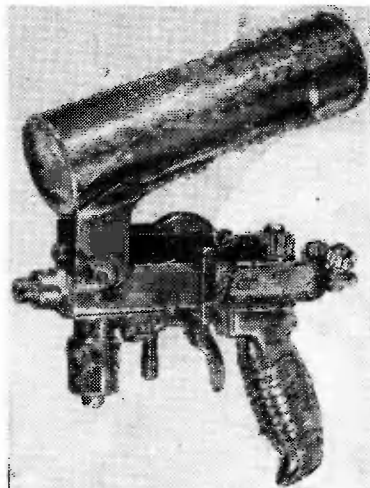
Аппарат Metco (США) для газопламенного напыления покрытий из тугоплавких металлов и керамики
